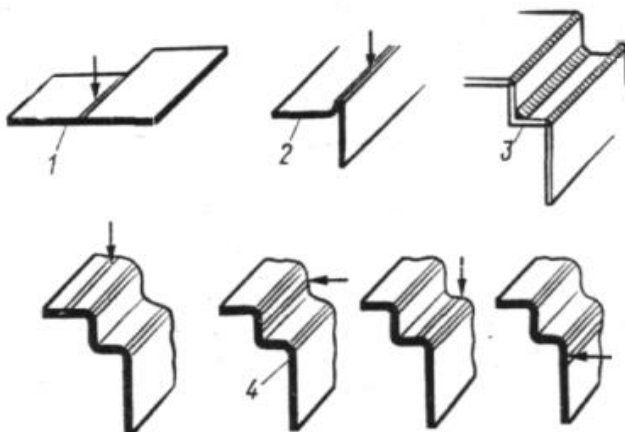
Виды сварных соединений: 1 - встык; 2 - с отбортовкой кромки; 3 - внутренний или наружные угловые швы; 4 - расположение сварочного шва, позволяющего производить рихтовку (показано стрелкой)
